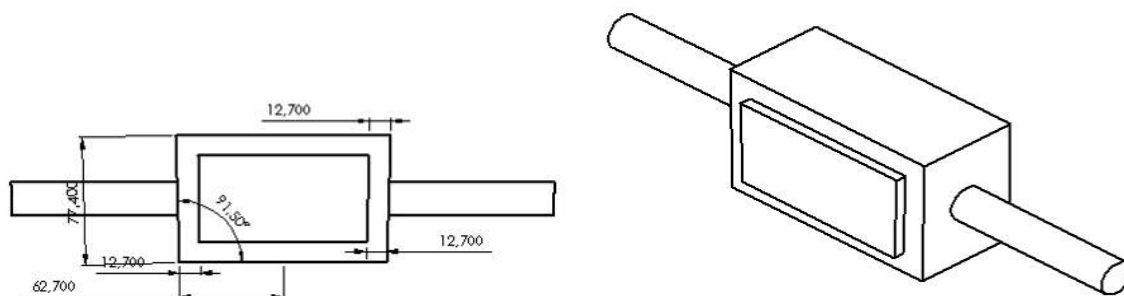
Desenho do molde refrigerado completo em CAD
